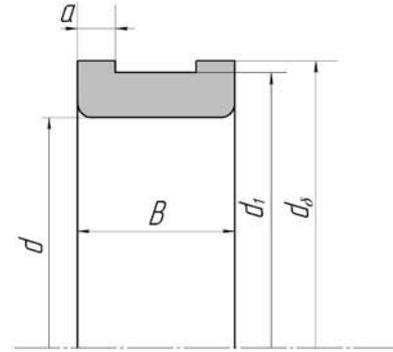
Основные размеры внутреннего кольца роликового подшипника
